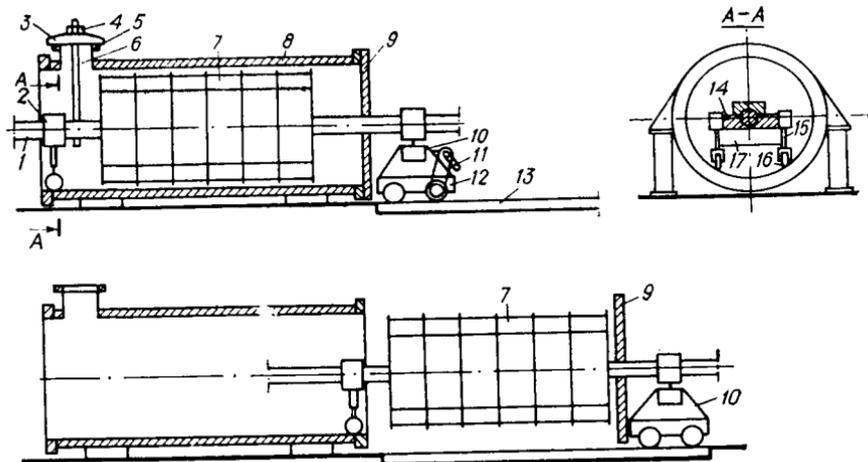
Приспособление для монтажа ротора горизонтального роторного аппарата:
